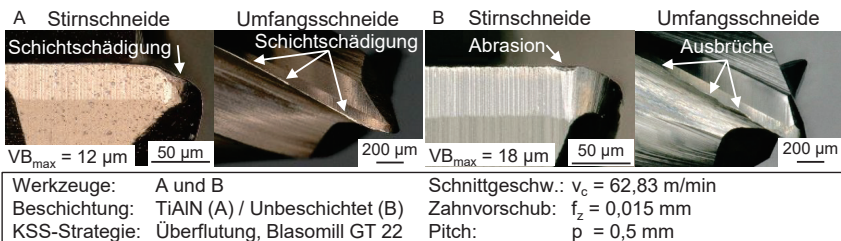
Werkzeugverschleiß beim Tauchfräsen von CuZn42 nach $l_{f,z} = 43,2$ m Vorschubweg je Schneide mit Werkzeugen A und B
